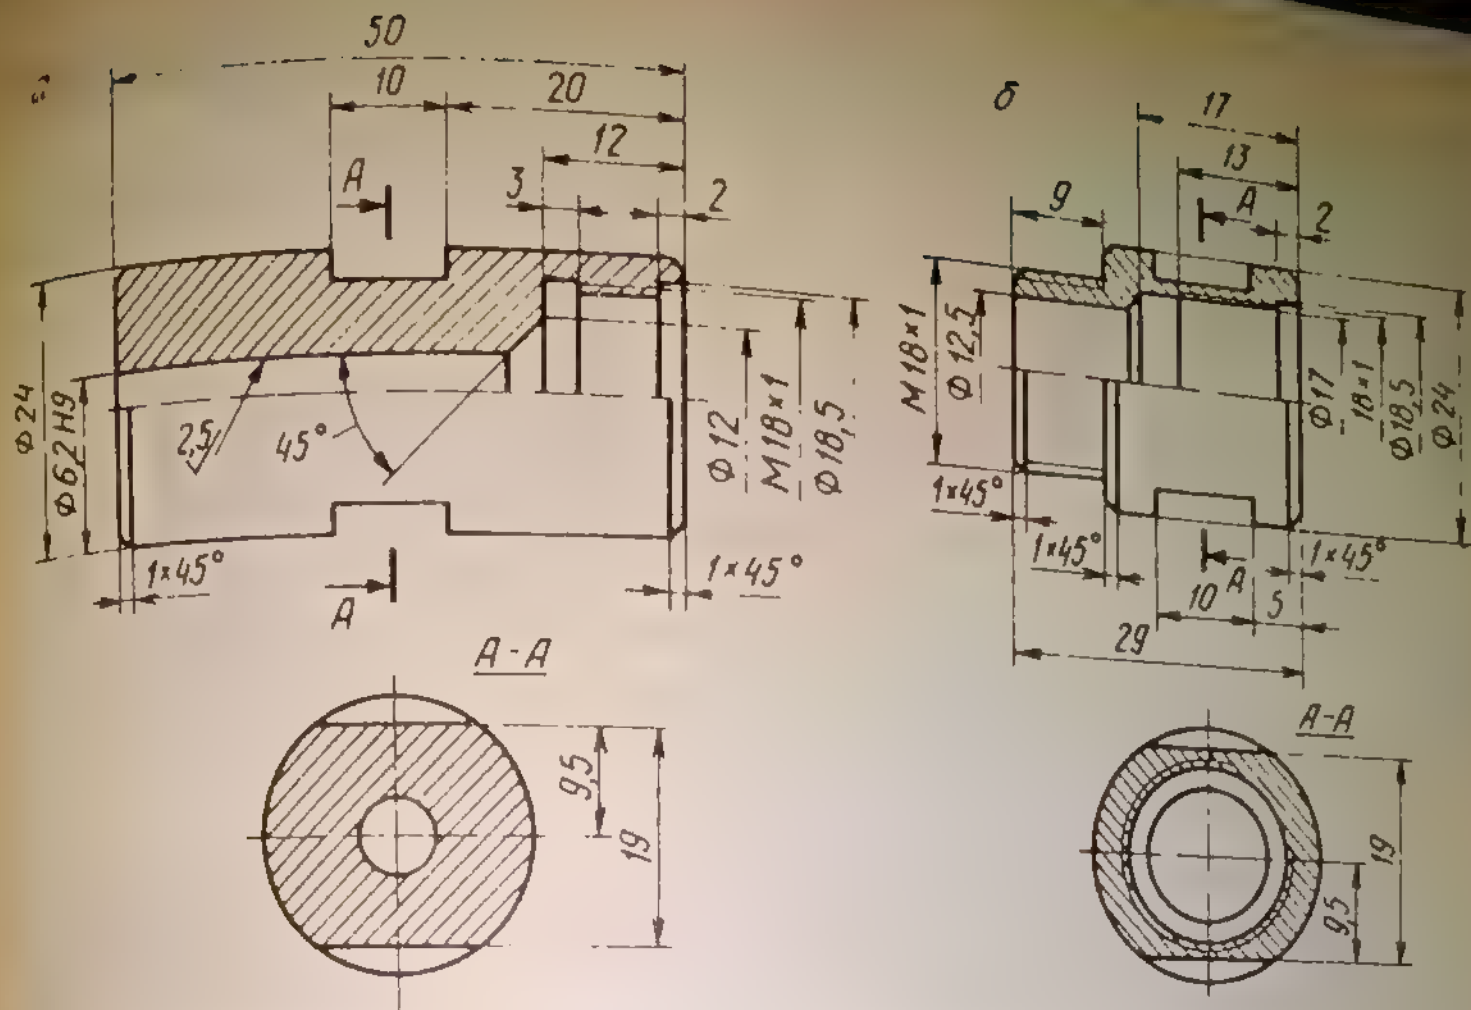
Приспособления для калибровки осевого отверстия в шпинделе вентильной головки с поворотно-поступательным движением клапана при модернизации
